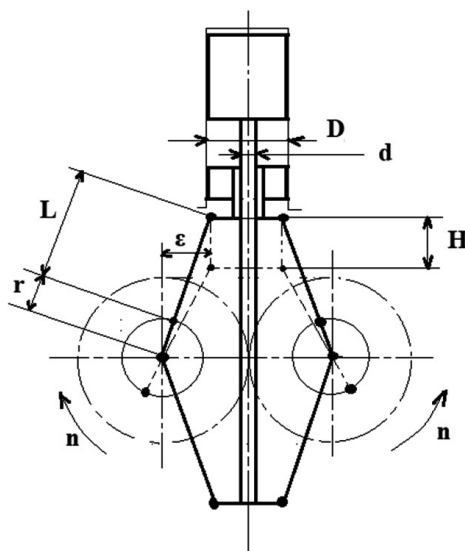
Кинематическая схема ромбического привода двигателя Стирлинга
